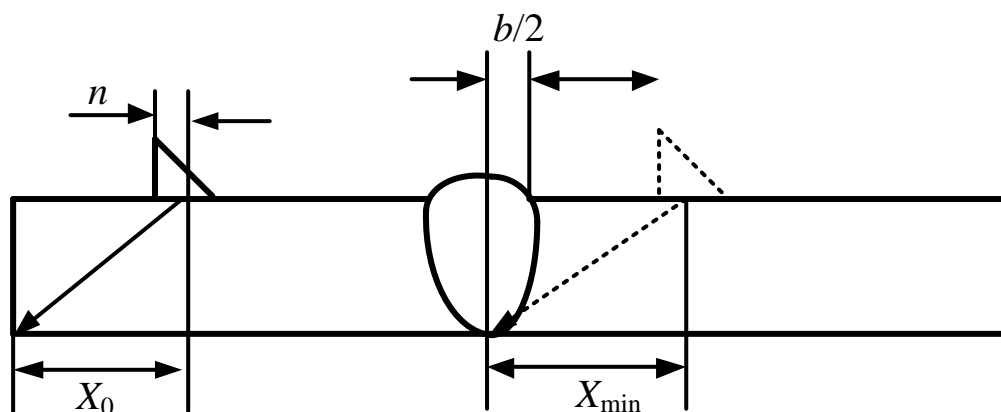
Схема прозвучивания сварного шва прямым лучом
